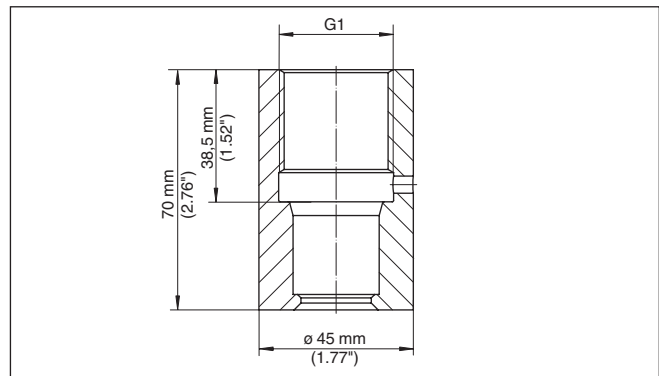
Maße Einschweißstutzen G1 geeignet für PASVE (für beide zuvor aufgeführte Ausführungen) - VEGABAR 82
